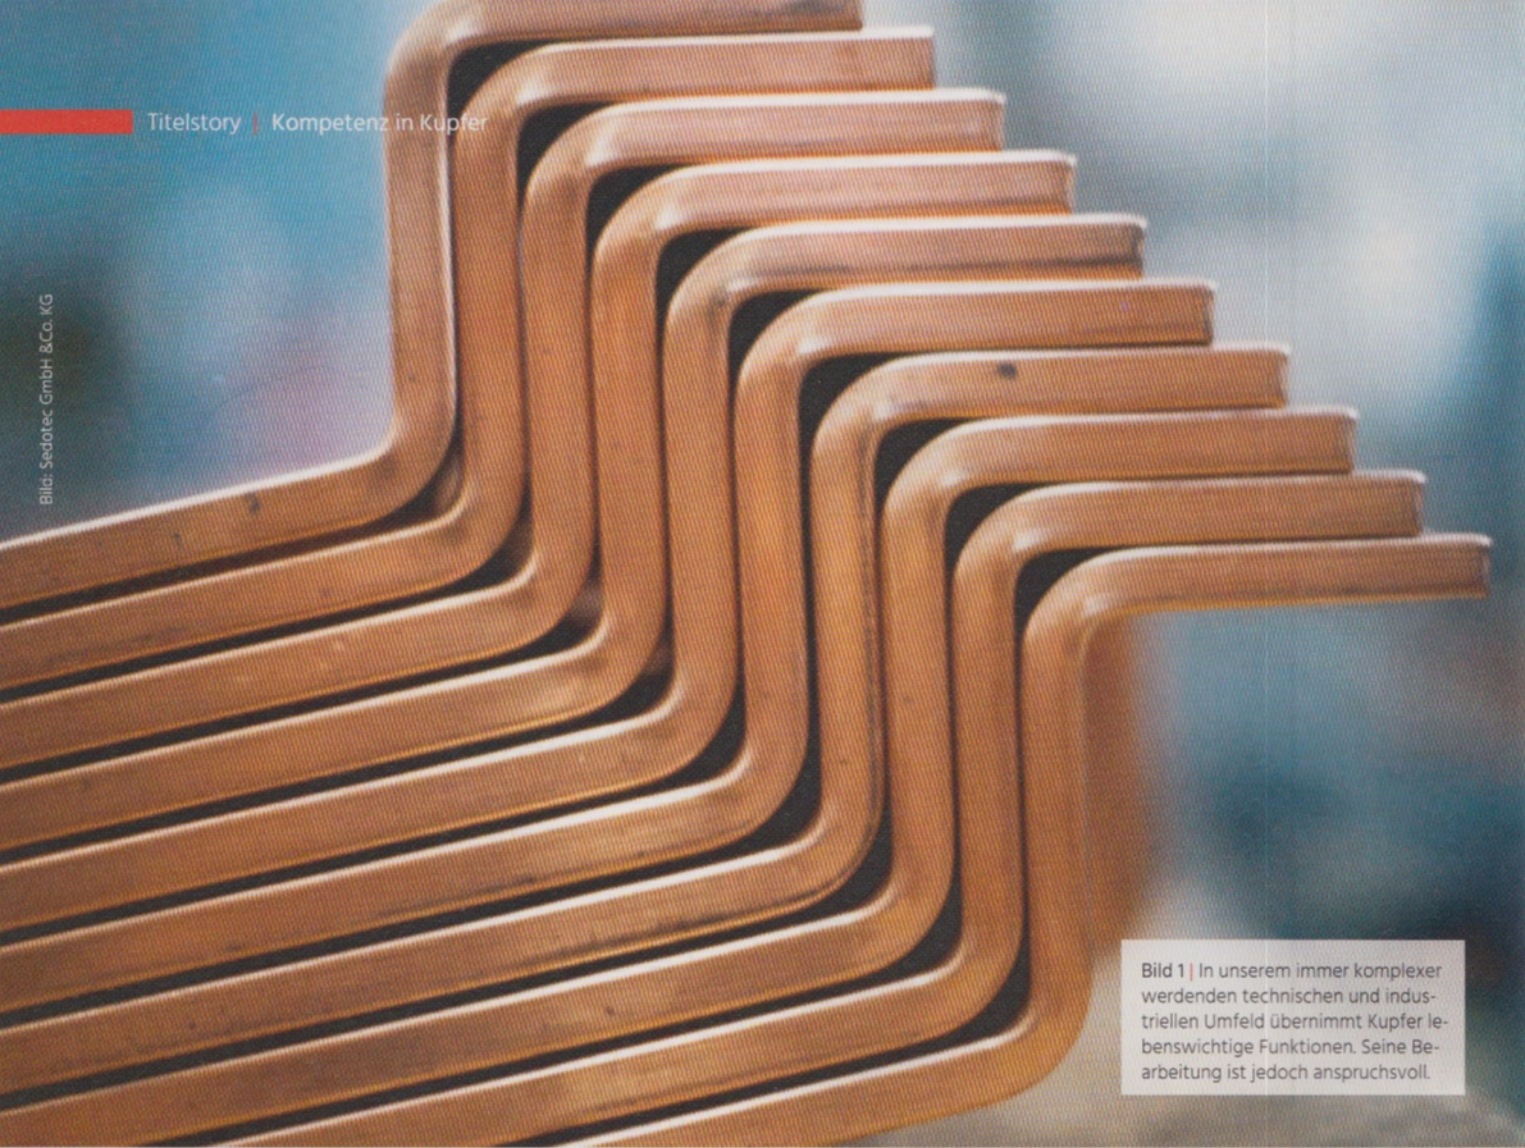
| In unserem immer komplexer werdenden technischen und industriellen Umfeld übernimmt Kupfer lebenswichtige Funktionen. Seine Bearbeitung ist jedoch anspruchsvoll.
